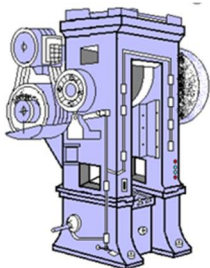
Кривошипний гарячештампувальний прес
